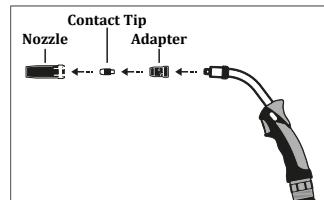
Retrait de la buse, du tube contact et de l'adaptateur
